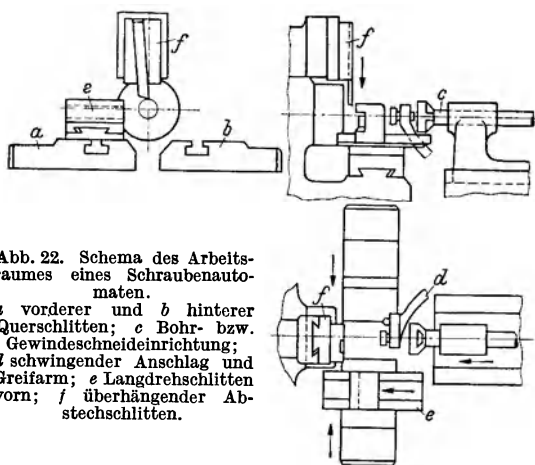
Schema des Arbeitsraumes eines Schraubenautomaten.
